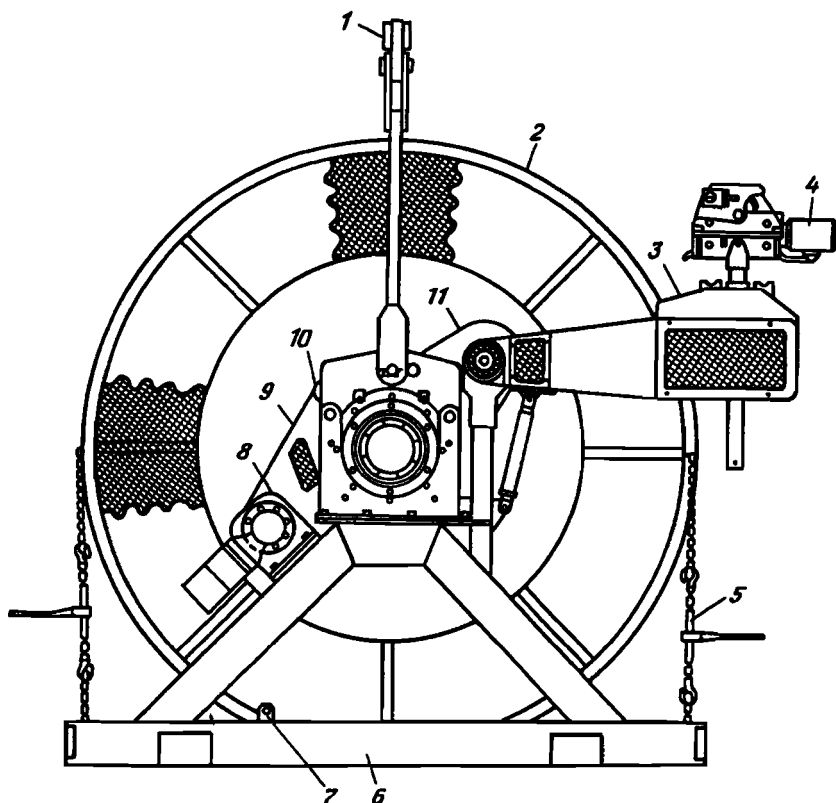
Конструкция барабана для хранения колонны гибких труб:
